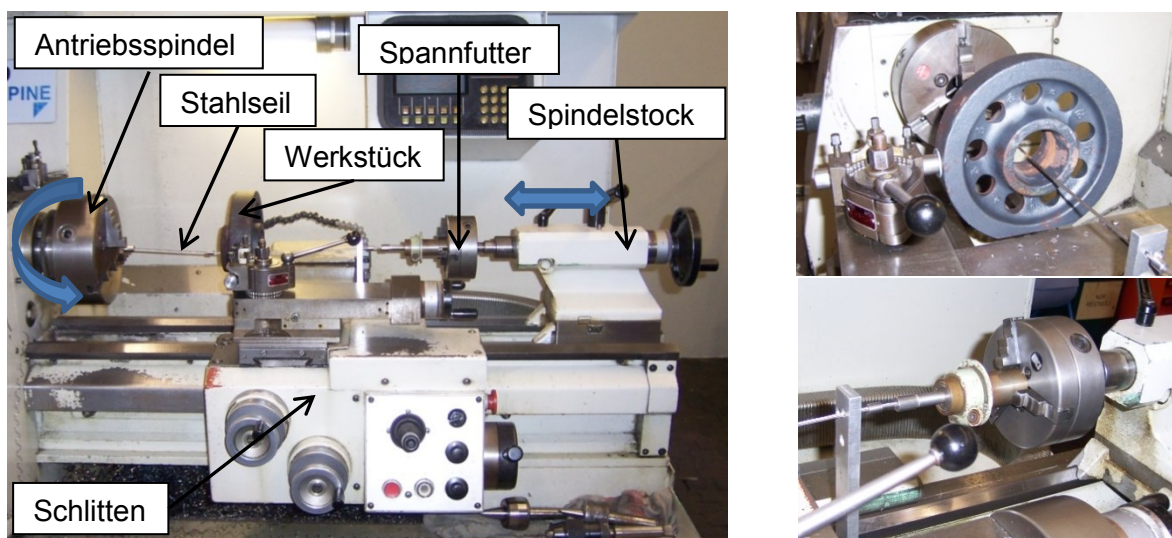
Prinzipieller Versuchsaufbau mit dem Seilwerkzeug zur Innenbearbeitung einer Zahnradnabe
